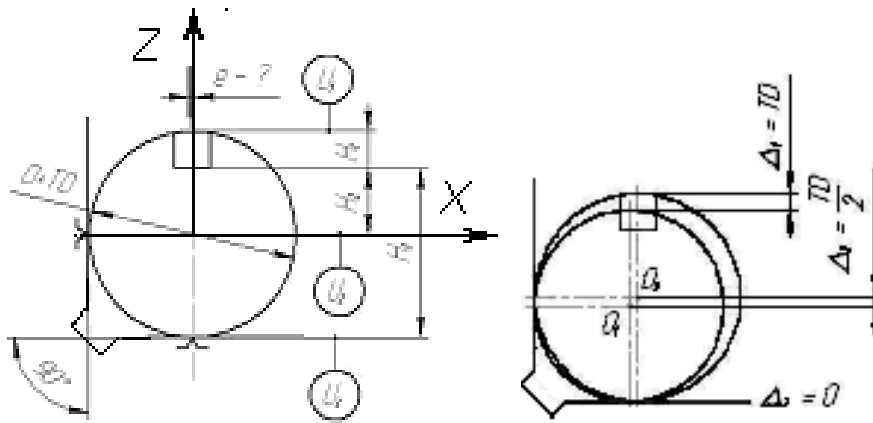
Розташування баз та розрахункова схема при встановленні деталі у похилий призмі
